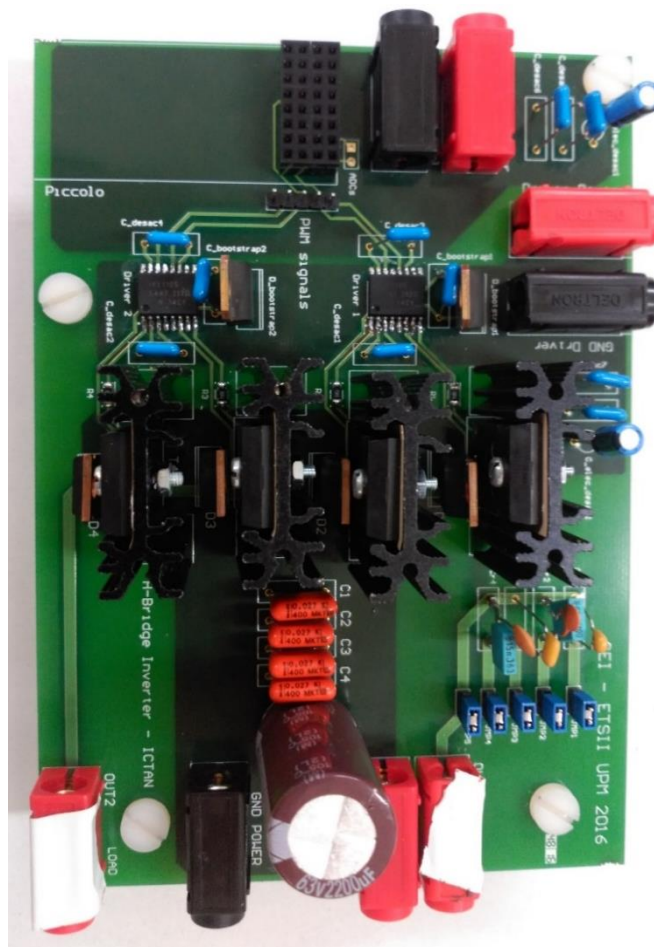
Vista en planta de la PCB después de soldadura y montaje de componentes
